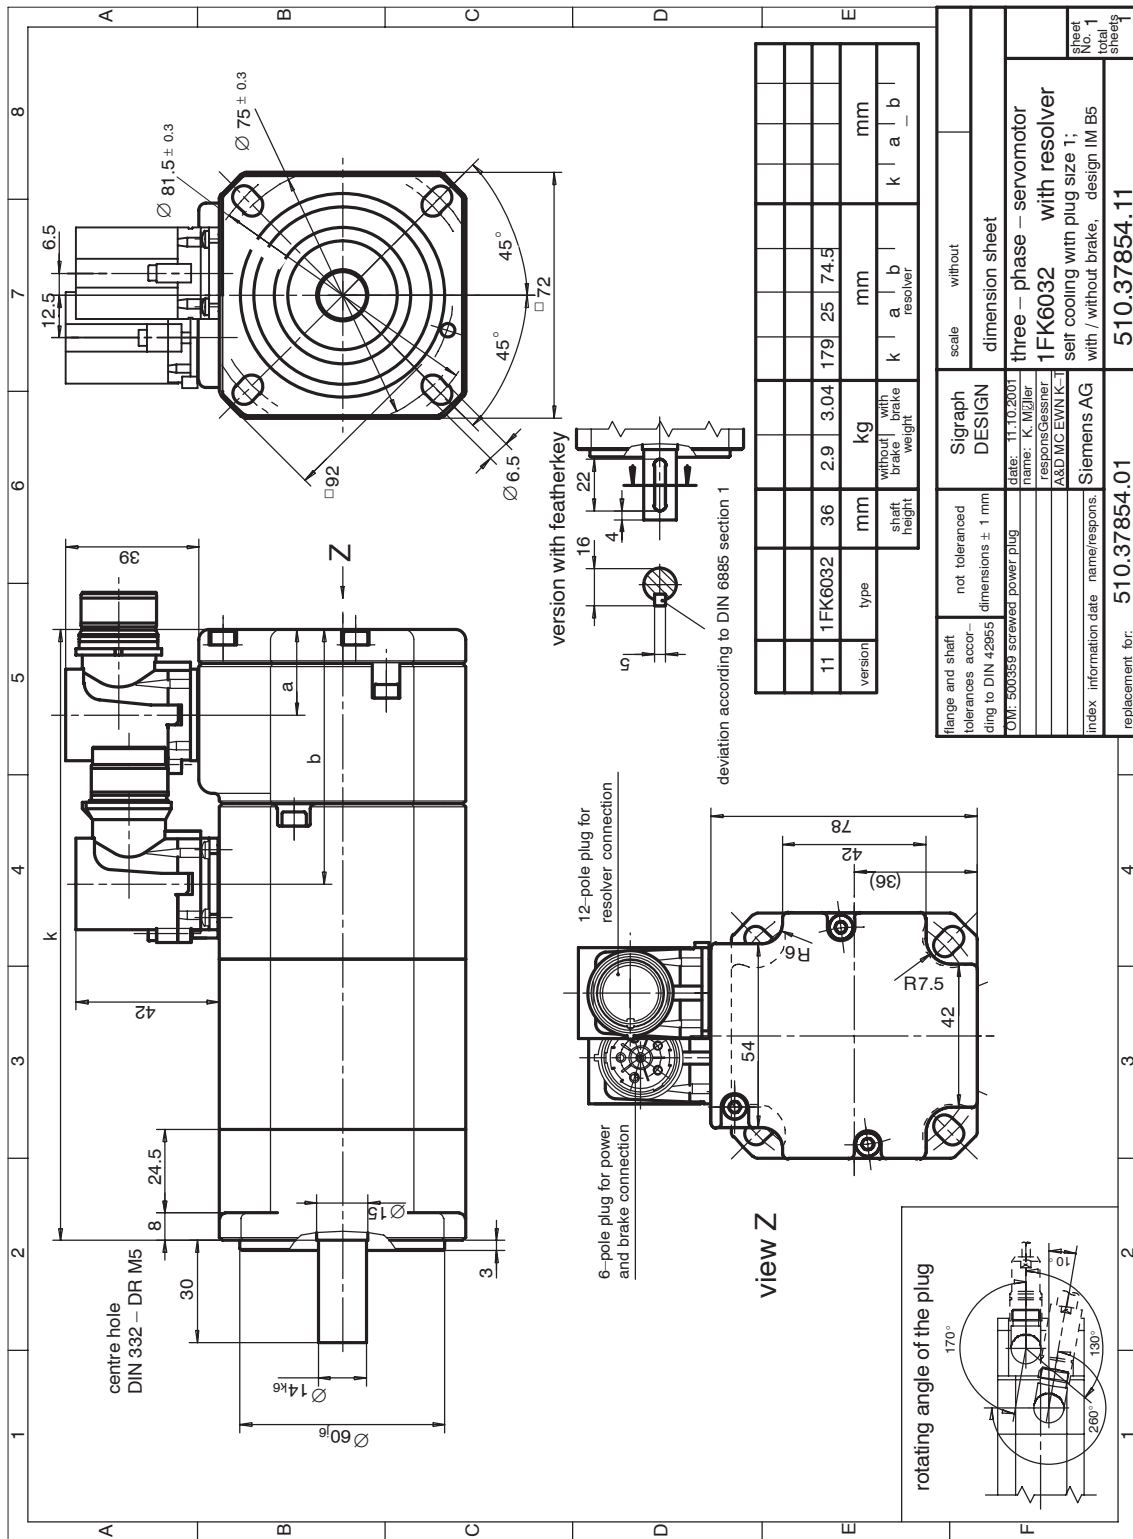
1FK6032 Standard, selbstgekühlt mit abgewinkeltem Stecker Größe 1
